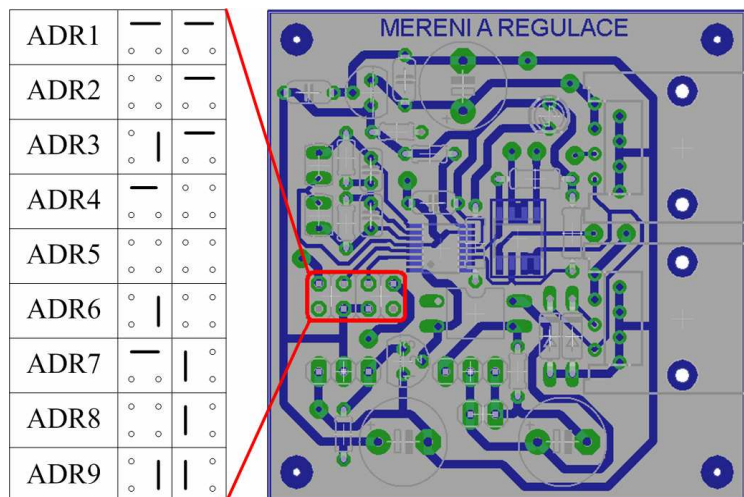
Realizovaná deska plošného spoje termostatu
